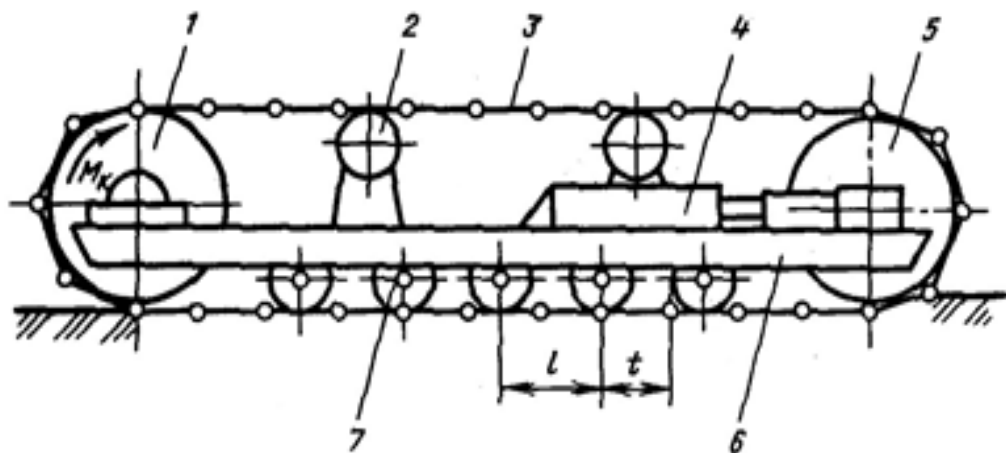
Многоопорный гусеничный движитель с жесткой подвеской опорных катков
